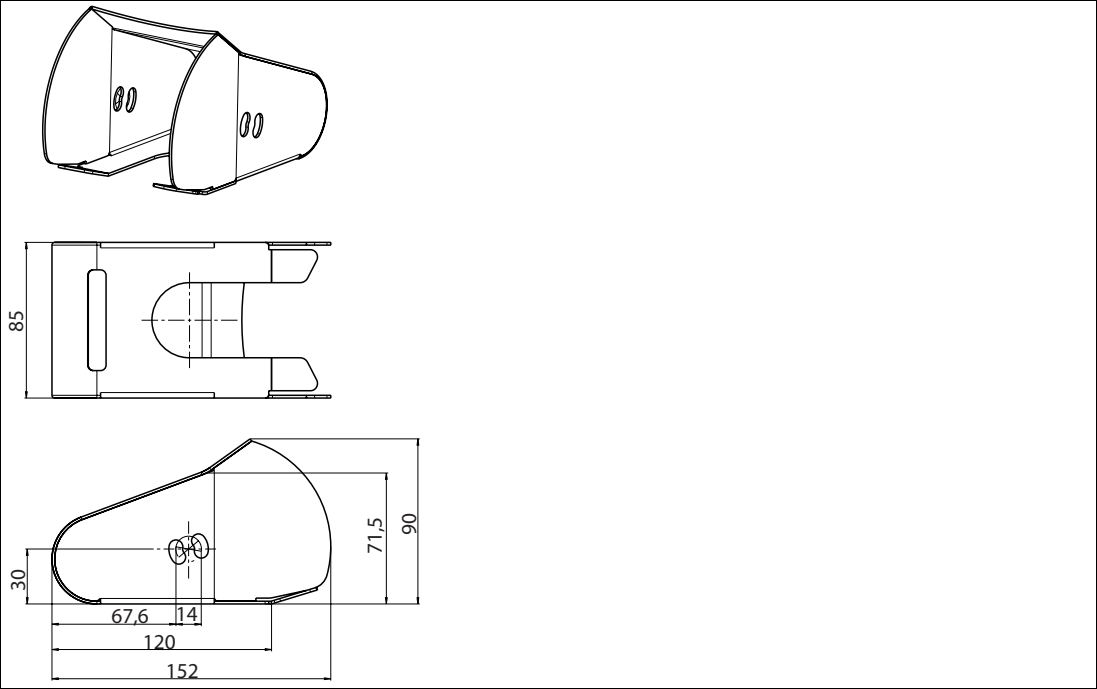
Abmessungen Halter für Barcode-Handheld
